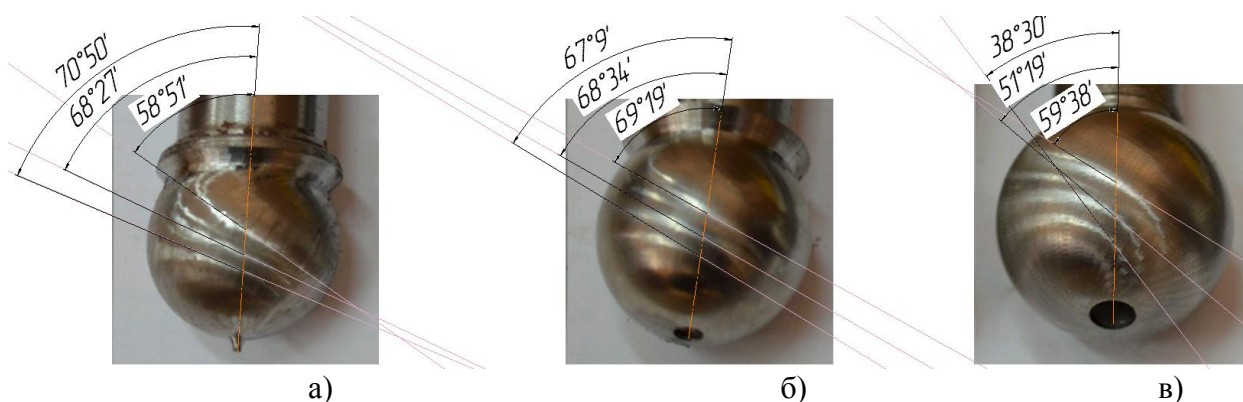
Вид сферической поверхности детали и углы наклона линий равной шероховатости:
